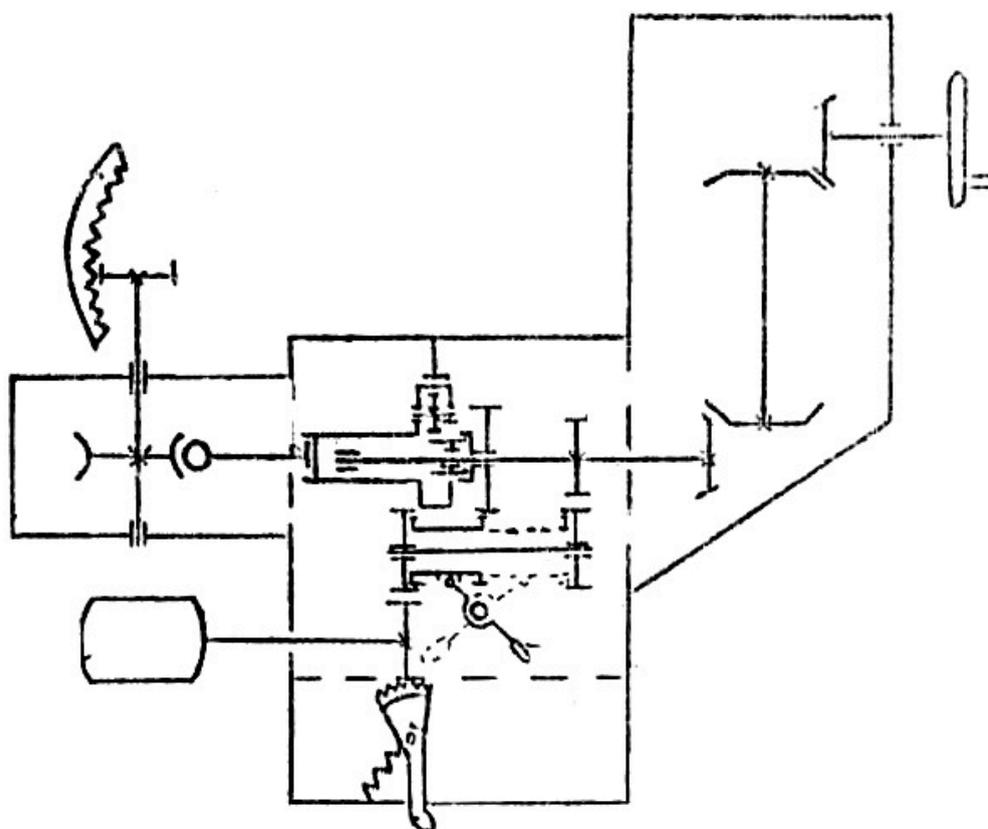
Кинематическая схема механизма вертикального наведения
